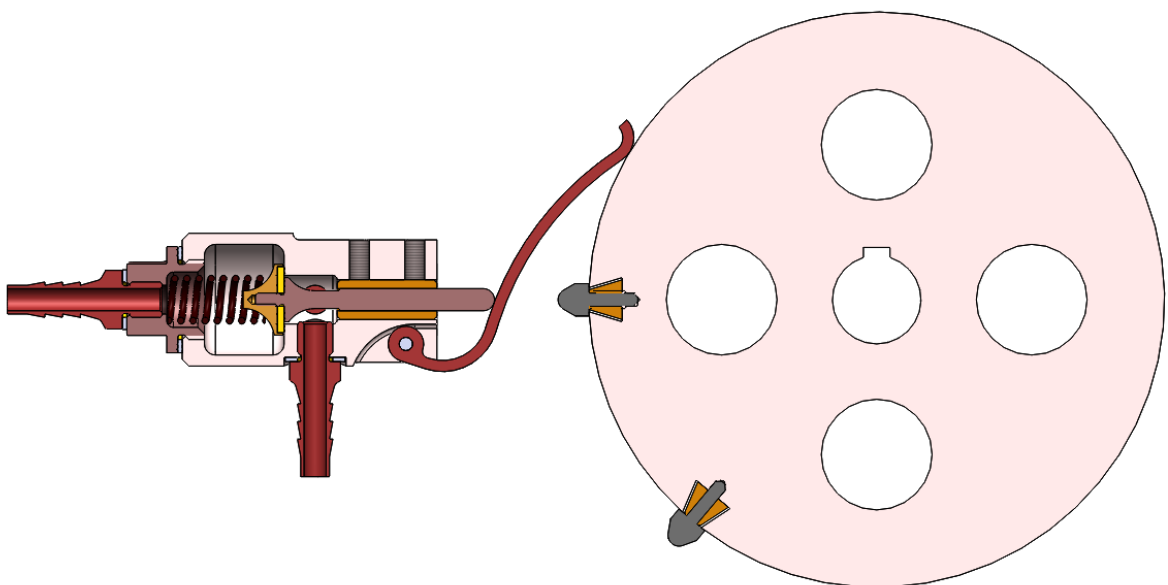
Пневматический сбрасыватель – разрез сборки
